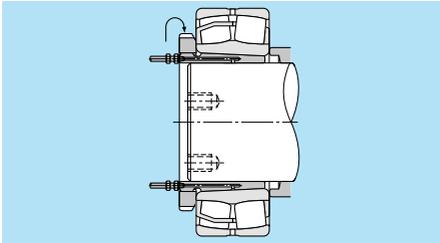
Demontage einer Abziehhülse mit Ölbohrungen
